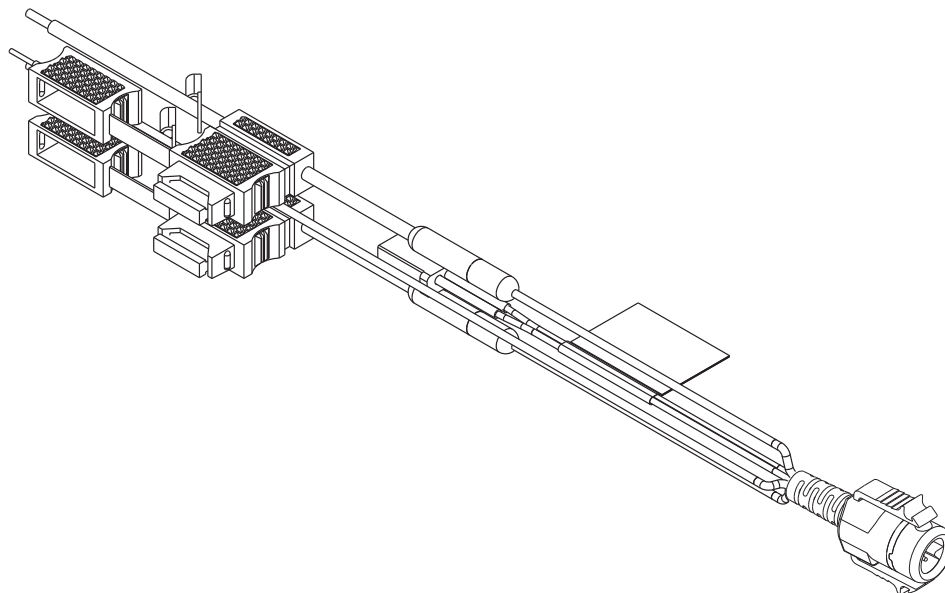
HKN6188_ Cabo de Alimentação com Conector de Alto-falante Externo
